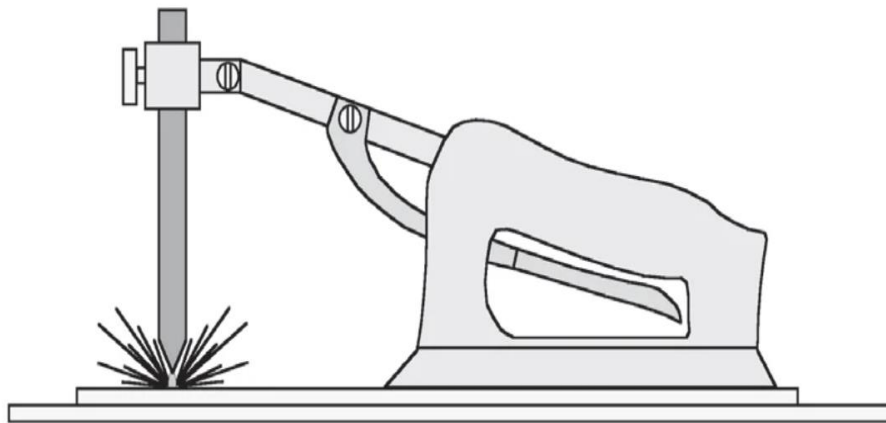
Sistema para soldagem a arco com eletrodo de carvão conforme a patente de Bernados.
